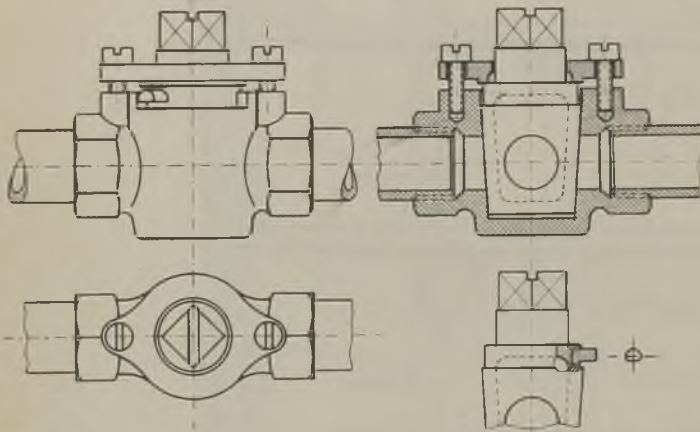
Haupt-Abstellhähnen für Gas mit Deckflansche.
